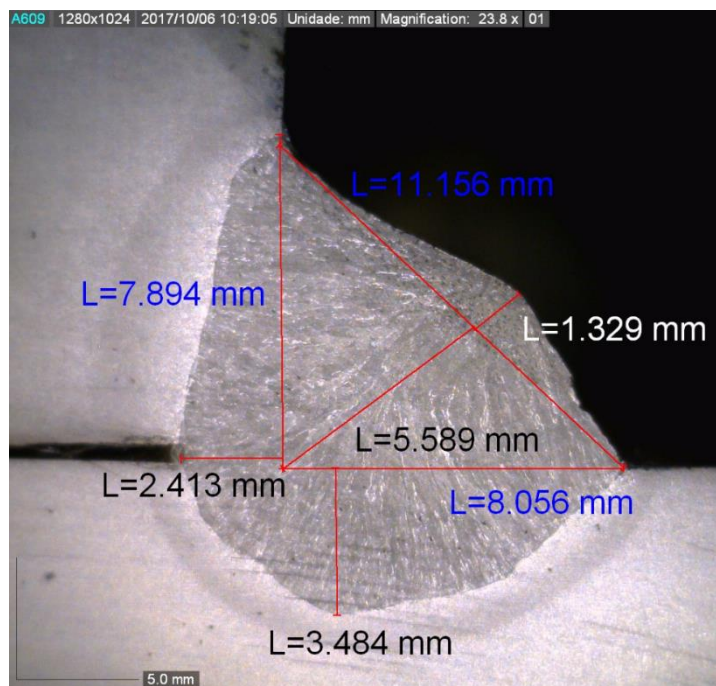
Macrografia de junta soldada com Arame Tubular.
